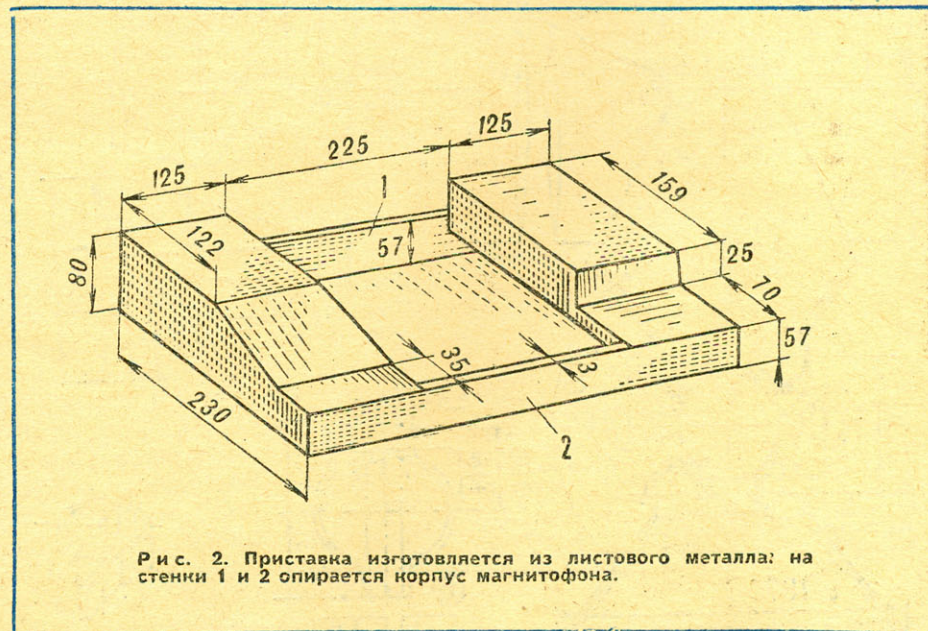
Приставка изготавливается из листового металла: на стенки 1 и 2 опирается корпус магнитофона.
